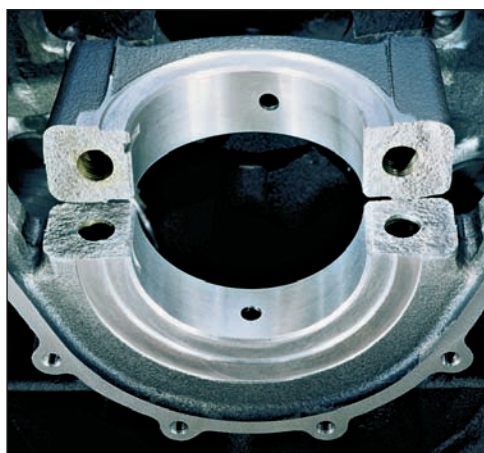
Крышки коренных подшипников коленчатого вала двигателя V8 BMW, изготовленные методом отламывания
